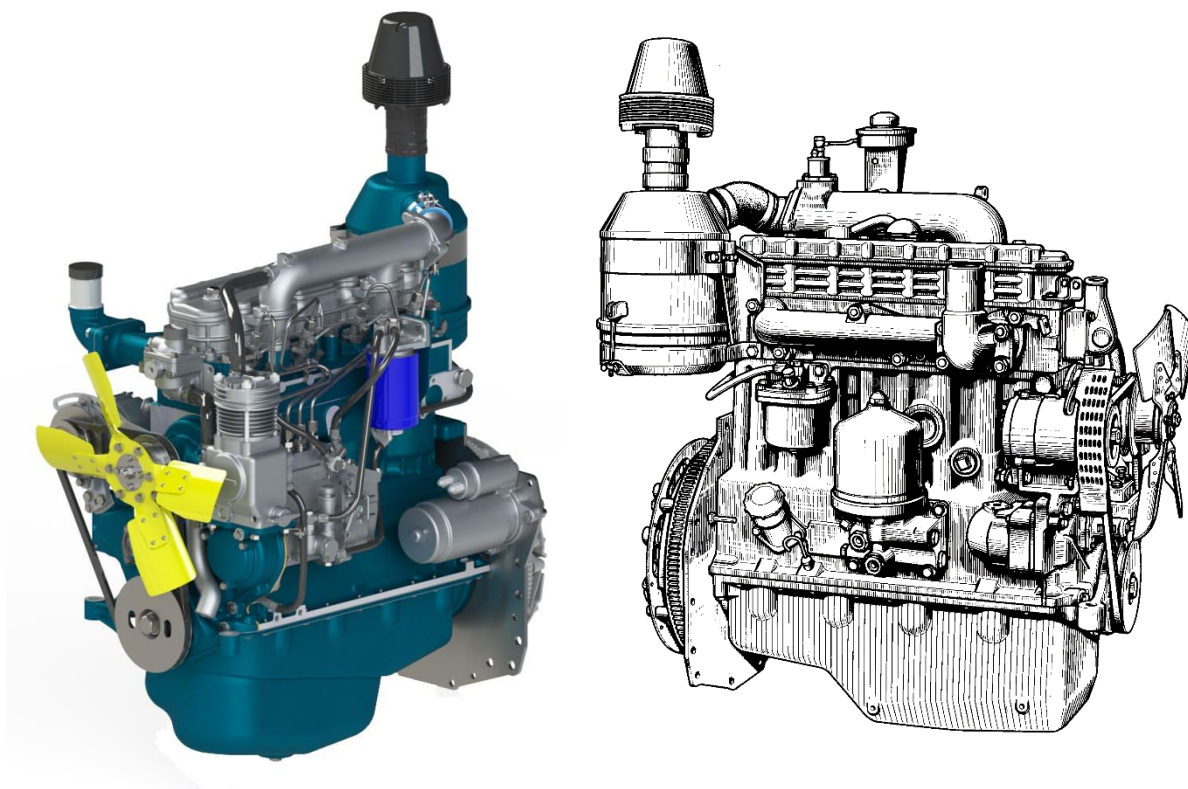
Силова установка дизель MMZ Д-243.91
